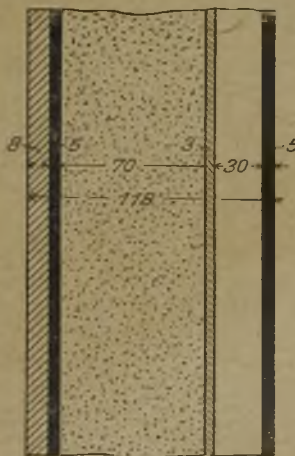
Wand einer Eisenkasse mit Stahlblechen
